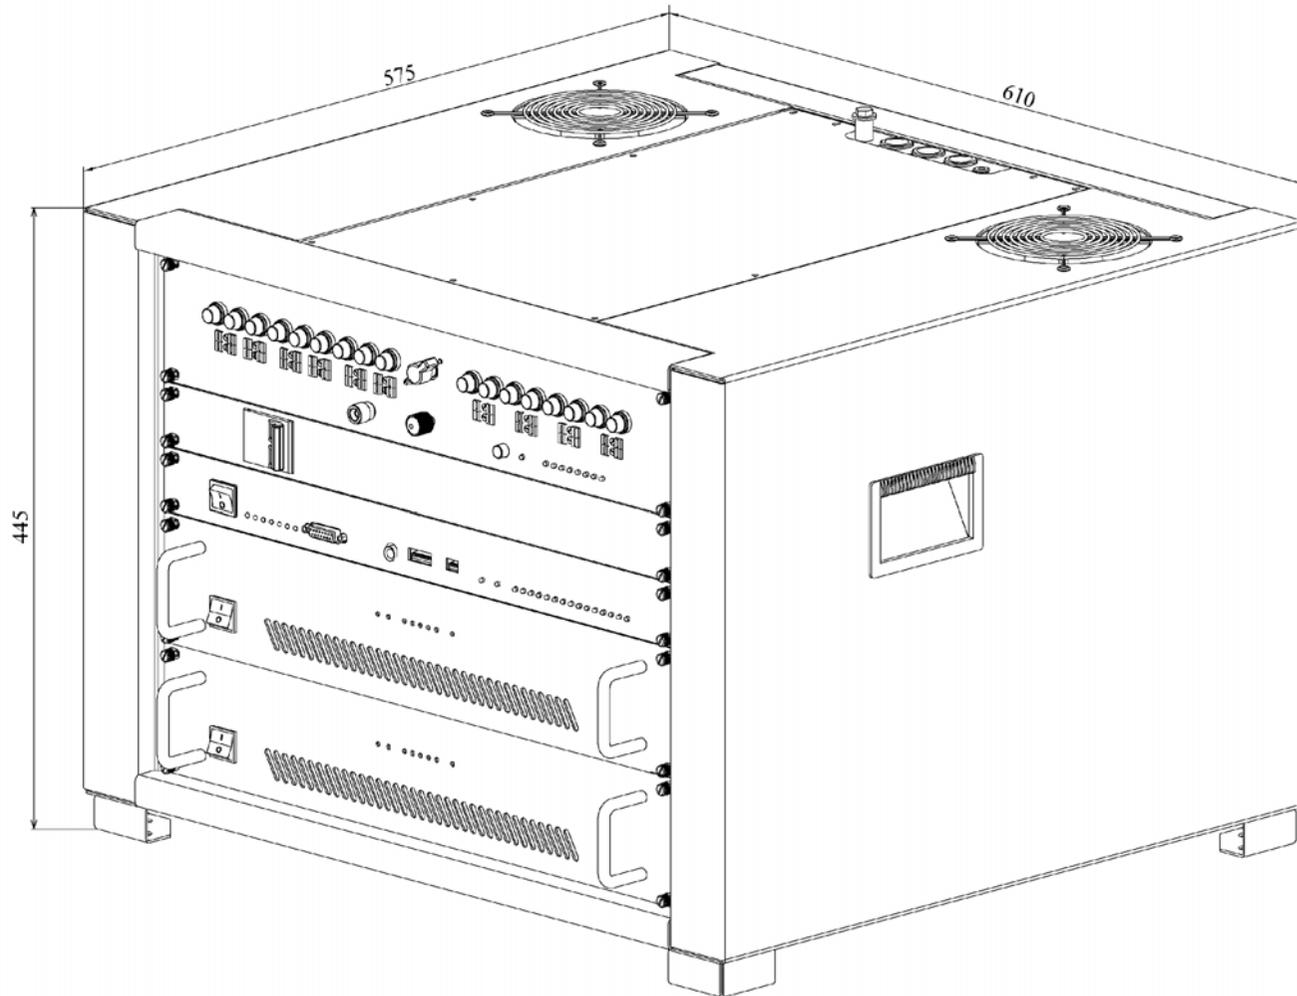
Внешний вид и габаритные размеры СКУ.М1
